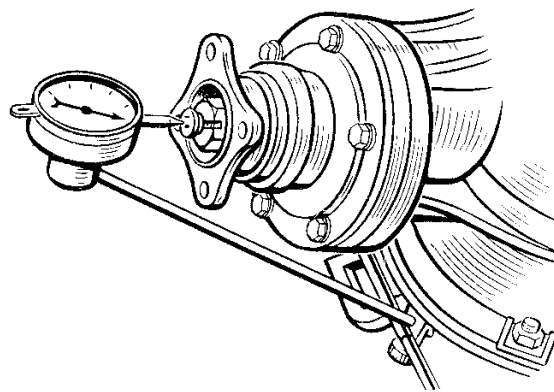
Определение осевого люфта в подшипниках ведущей шестерни главной передачи
